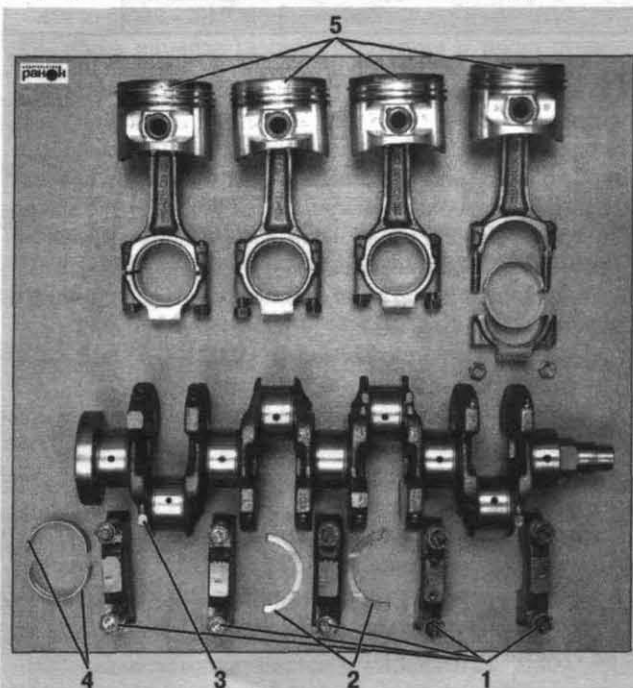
Детали кривошипно-шатунного механизма: 1 – крышки коренных подшипников коленчатого вала; 2 – полукольца упорного подшипника коленчатого вала; 3 – коленчатый вал; 4 – комплект коренных вкладышей; 5 – поршни в сборе с шатунами
